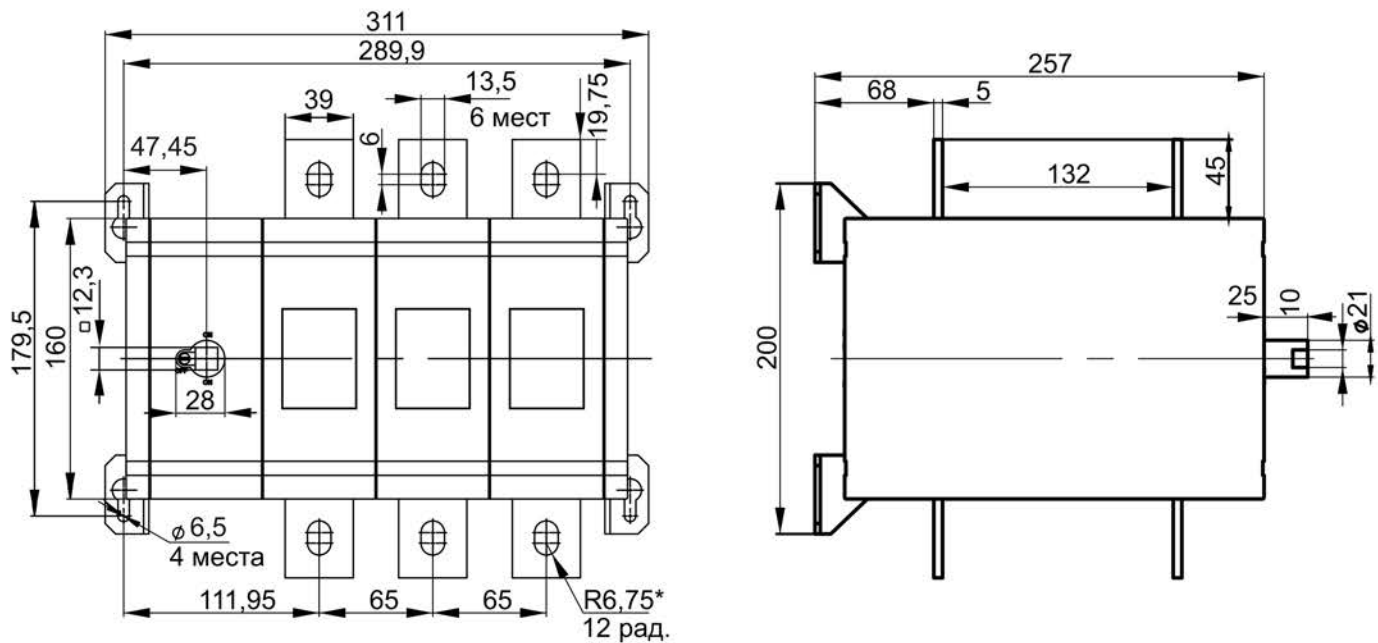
Габаритные, установочные и присоединительные размеры реверсивных ВРК 630–800 А / Figure 7 – Overall, mounting and connection dimensions of reverse VRK 630–800 A
